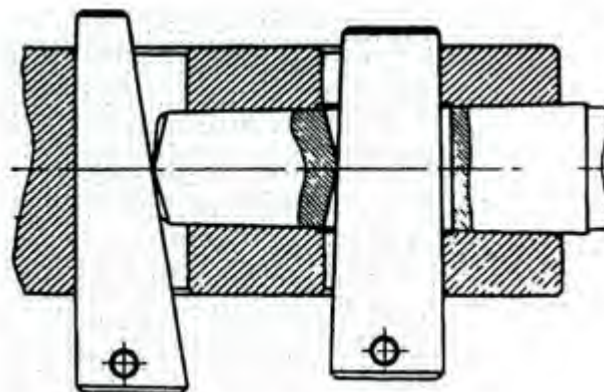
Закріплення інструмента в шпинделі розточувального верстата
